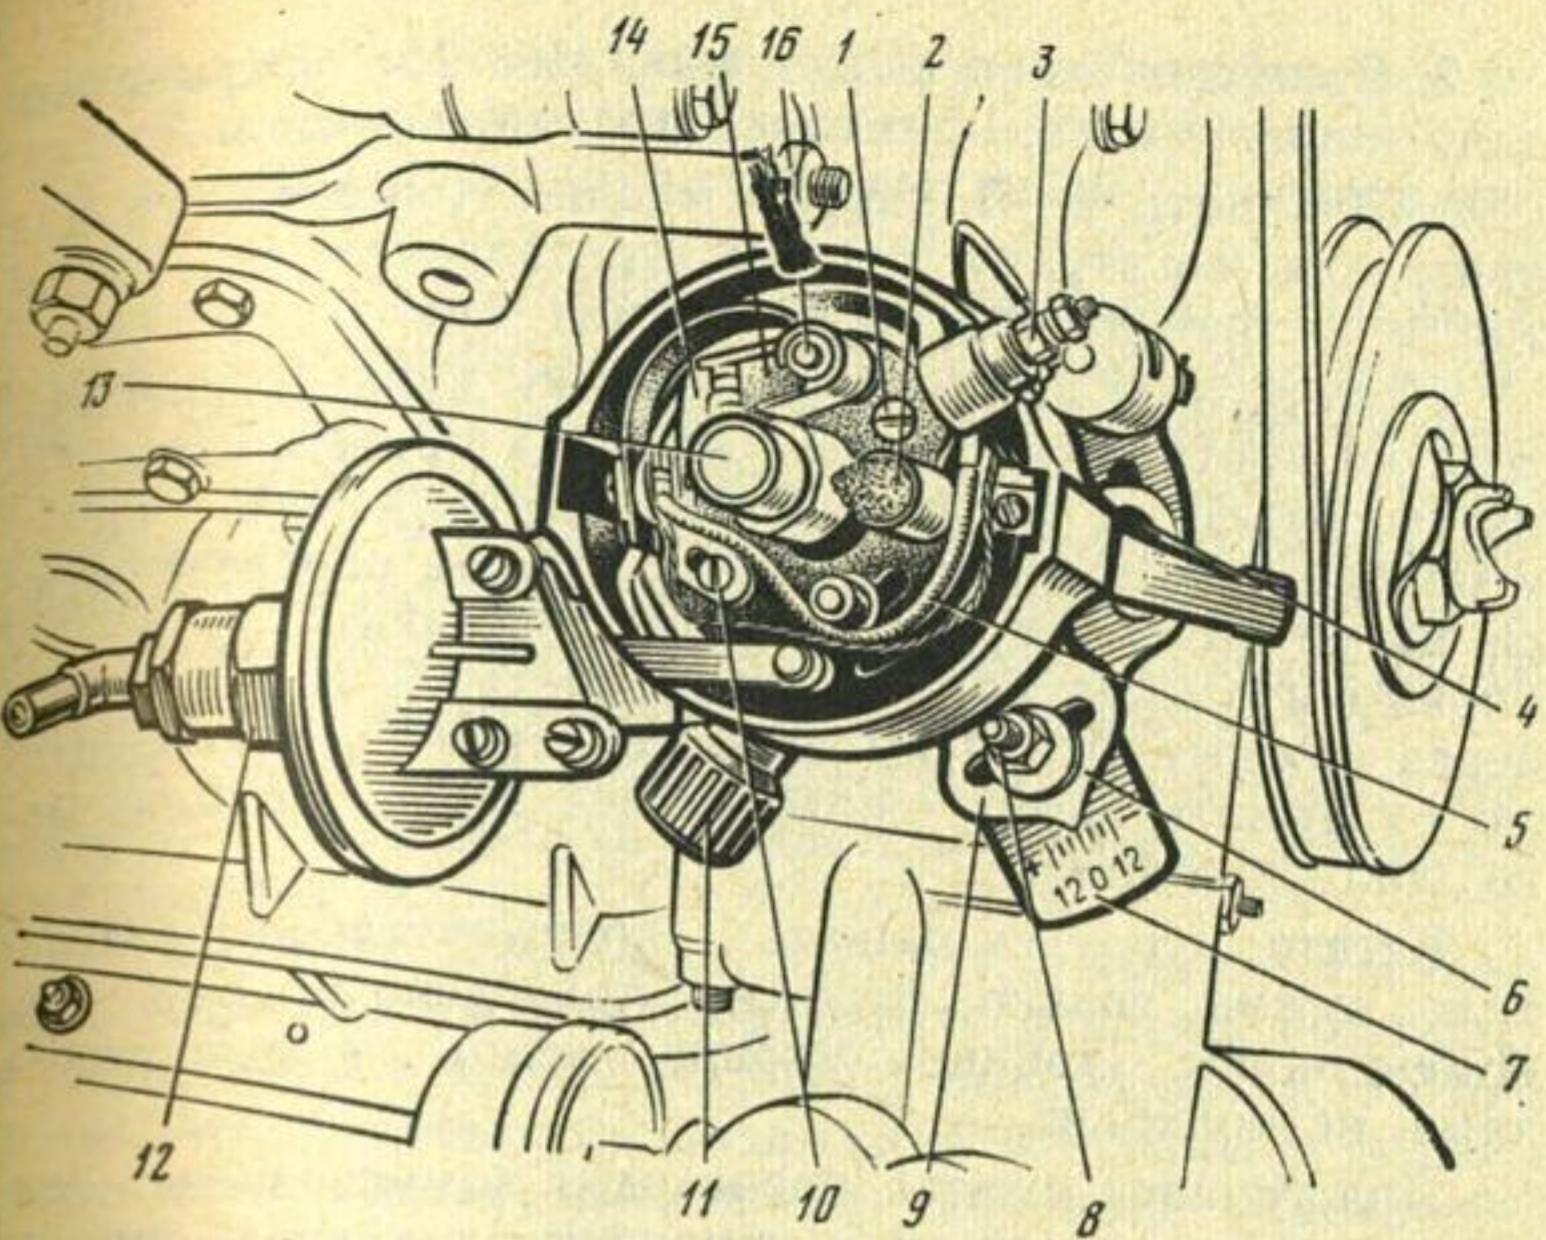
Распределитель зажигания (со снятыми крышкой и ротором):
